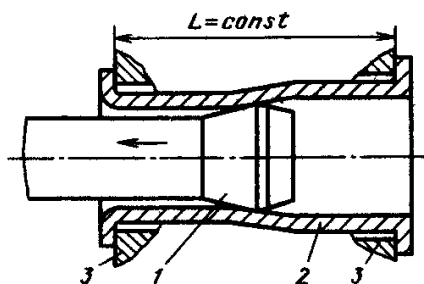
Обработка с осевым заневоливанием детали: 1 — инструмент; 2 — деталь; 3 — опоры
